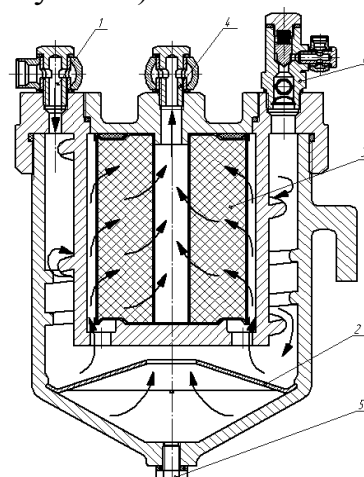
Фильтр тонкой очистки топлива: 1 – подводящий штуцер; 2 – успокоитель; 3 – фильтрующий элемент; 4 – отводящий штуцер; 5 – сливной болт; 6 – воздушный клапан
